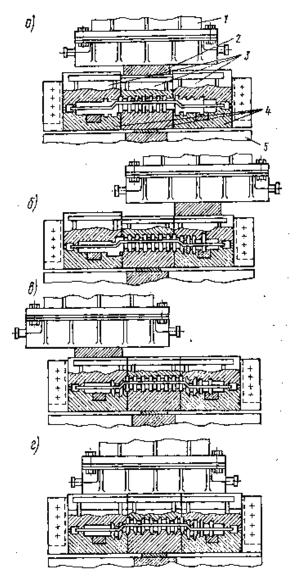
Схема секционной штамповки крупного коленчатого вала на гидравлическом прессе: а, б, в – соответственно штамповка средней правой и левой частей; г – калибровка готовой поковки всеми секциями штампа; 1 – траверса; 2 – накладка; 3, 4— секции соответственно верх-
